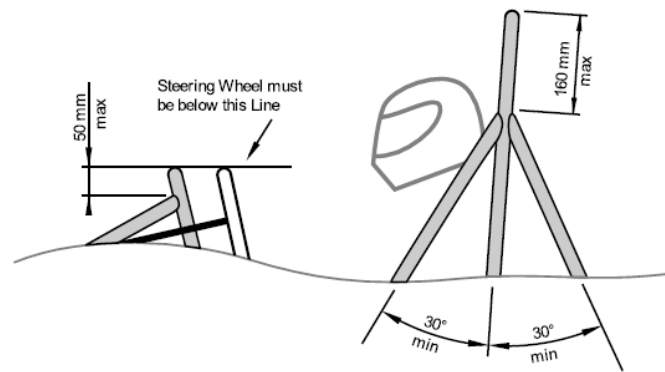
Requisits dels suports del cercol principal i frontal. FSAE Rules 2021 [2].
